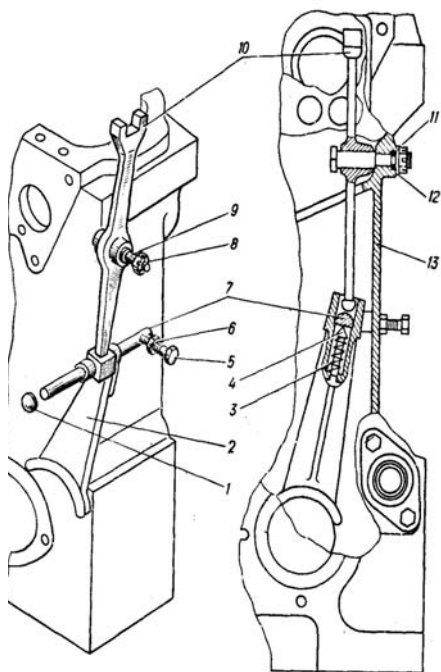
Снятие механизма включения переднего моста: 1 — заглушка; 2 — вилка; 3 — пружина; 4 — фиксатор; 5 — болт; 6, 8 — гайка; 7 — валик; 9 — ось; 10 — рычаг; 11 — кольцо; 12 — шайба; 13 — корпус
